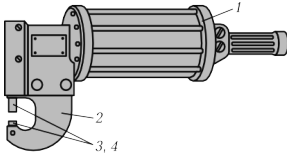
Ручний переносний пневматичний прес: 1 – циліндр; 2 – скоба; 3, 4 – обтискачі
